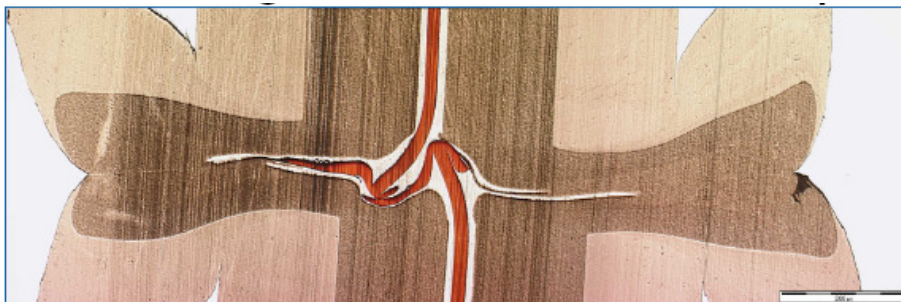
Verschweißung von HDPE-Mehrschichtplatten [37]
